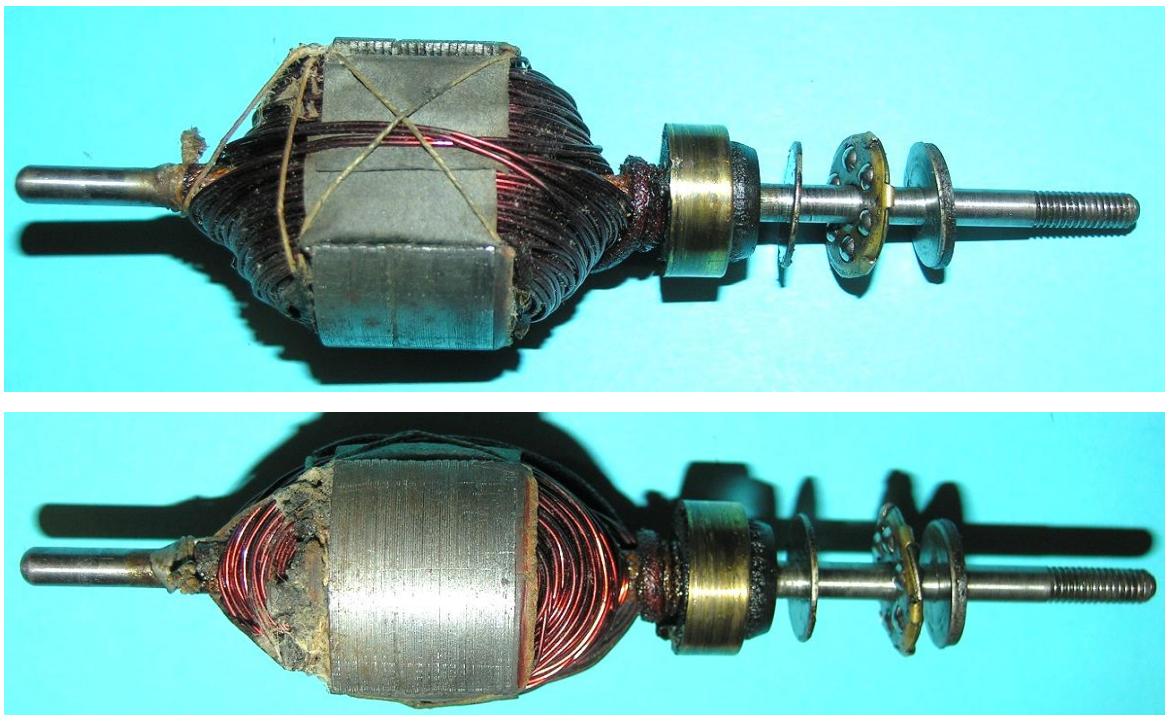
Anker mit 4 mm-Welle, Schleifring und Axiallager, Durchmesser des Ankerblechpakets 31,4 mm
